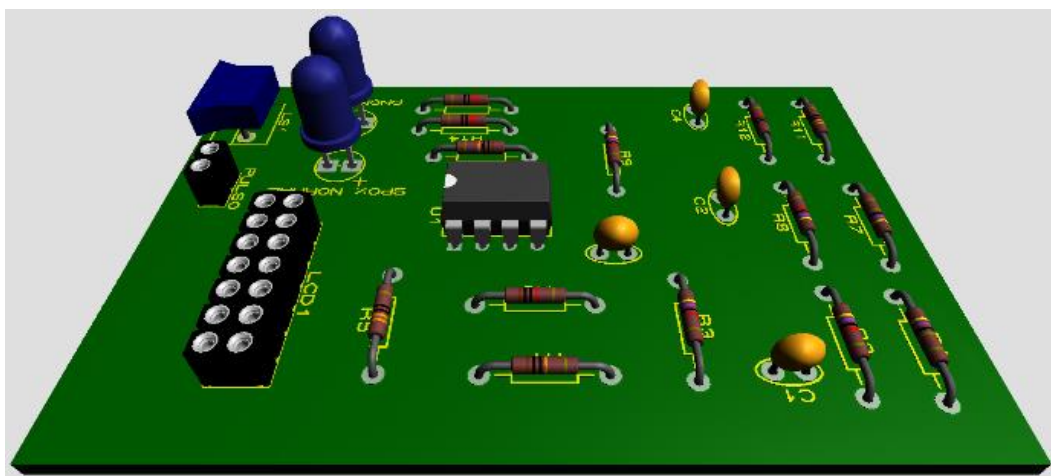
Vista Trasera de Circuito en Placa PCB
